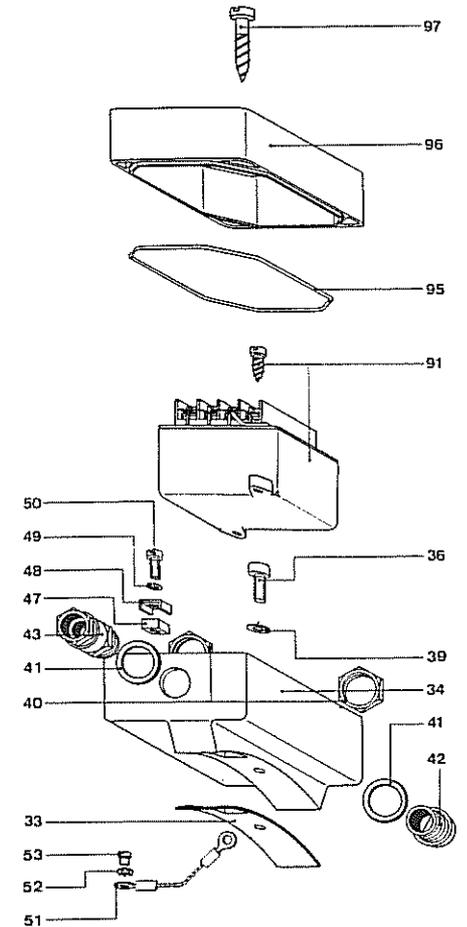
Anschlußgehäuse mit Gleichrichter mit Übererregung
